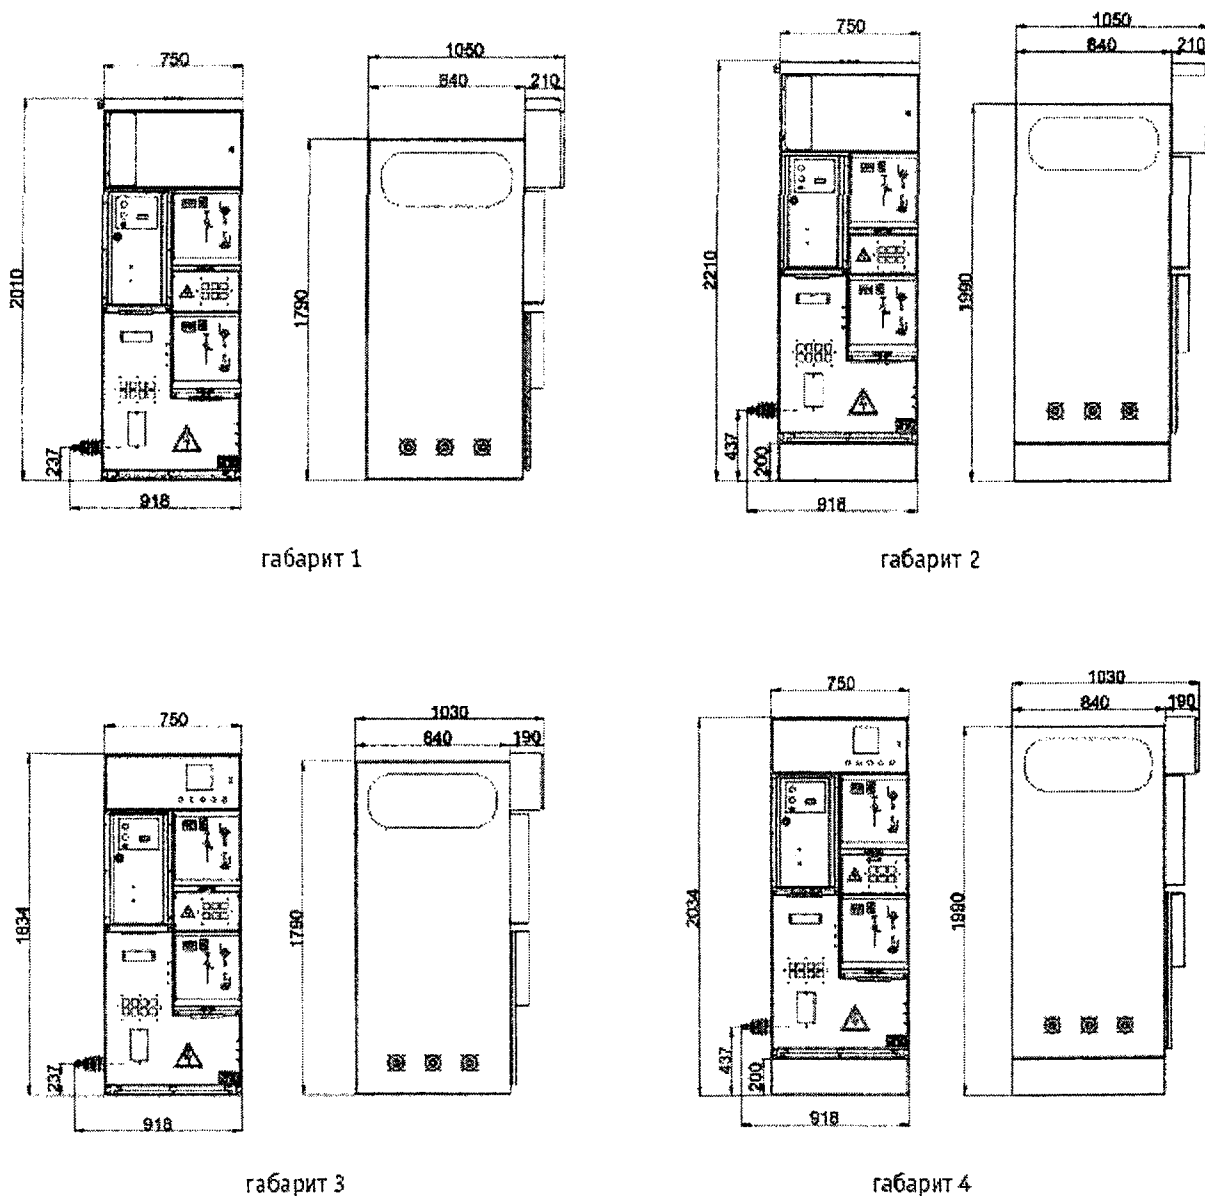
Общий вид ячейки КСО, габаритные, установочные и присоединительные размеры, на примере ячейки с вакуумным выключателем и двумя разъединителями (шинным и линейным)
